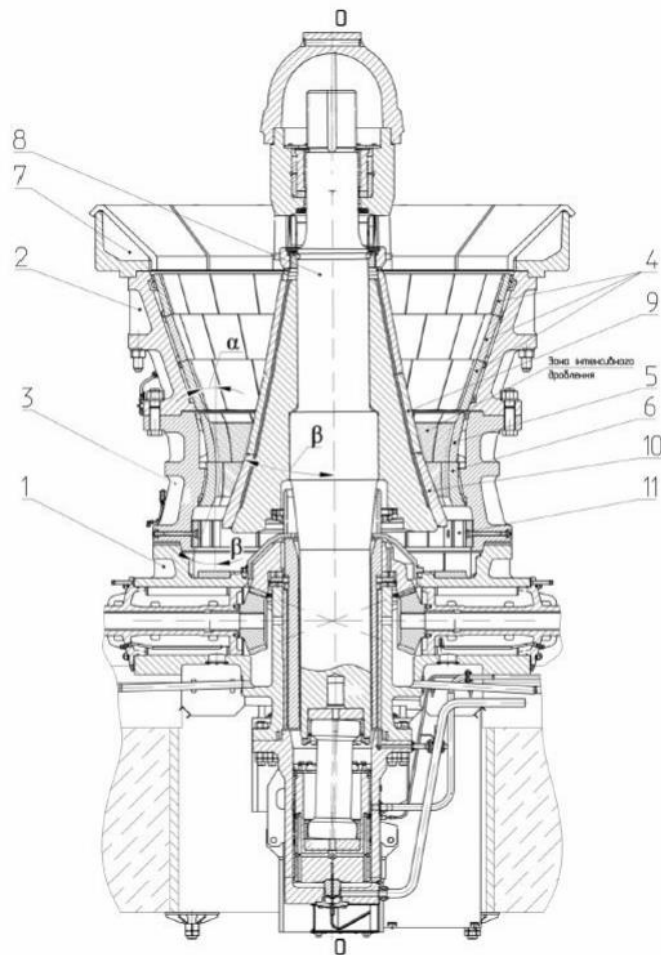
повздовжній переріз конусної дробарки крупного дроблення:
